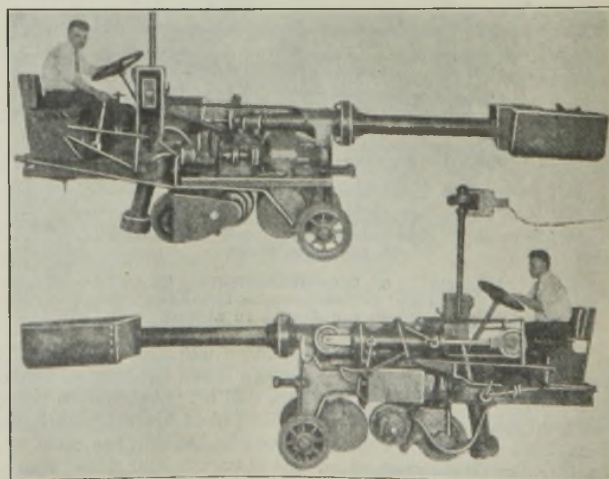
Auf Flur laufende gleislose Einsatzmaschine für Oefen.
